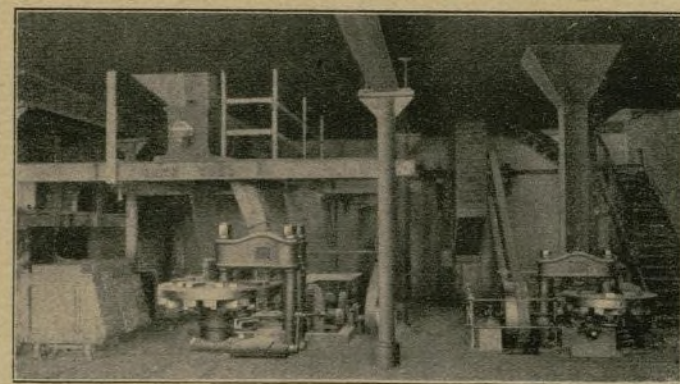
Instalación para la fabricación de piedras artificiales de arena y cal.
